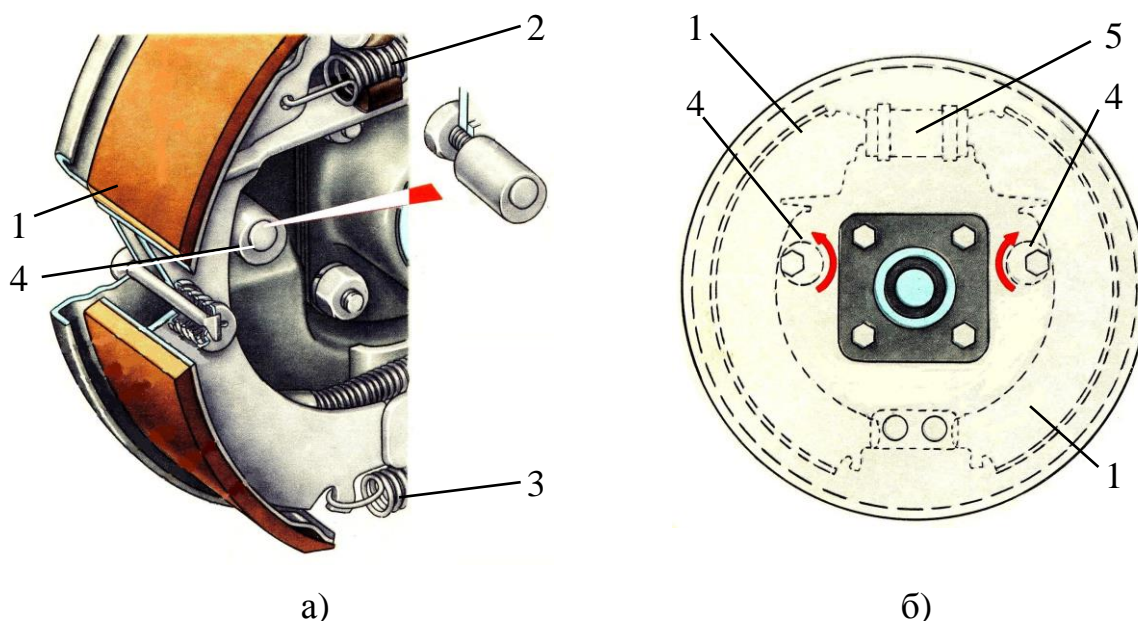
Конструкция устройства ручной регулировки для барабанного тормозного механизма с поршневым разжимным устройством (а), вид на тормозной механизм со стороны опорного диска (б): 1 – тормозные колодки; 2 и 3 – стяжные пружины; 4 – эксцентрики; 5 – разжимное устройство
